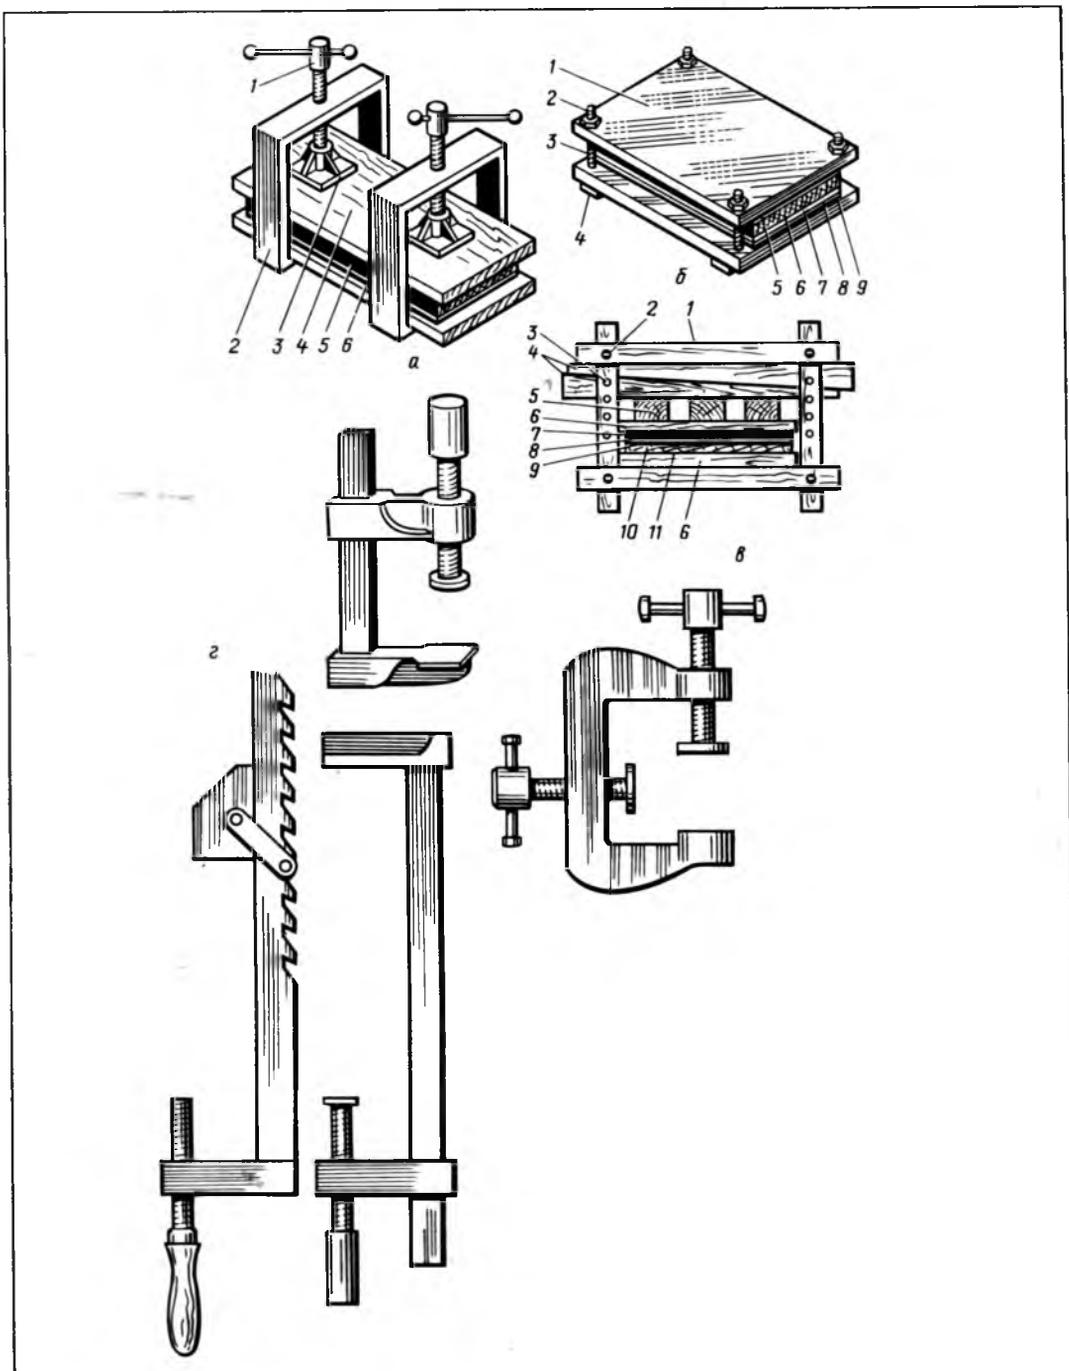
Приспособления и инструменты для склеивания (прессы и струбцины): а — пресс с хомутовыми струбцинами (1 — винт; 2 — рамка струбцины; 3 — пятка винта; 4 — деревянная плита; 5 — мозаичный набор; 6 — пористая резина); б — пресс на стяжных болтах (1 — металлическая или деревянная плита; 2 — гайка; 3 — болт; 4 — головка болта; 5 — облицовочная «рубашка» тыльной стороны набора; 6 — осно-
